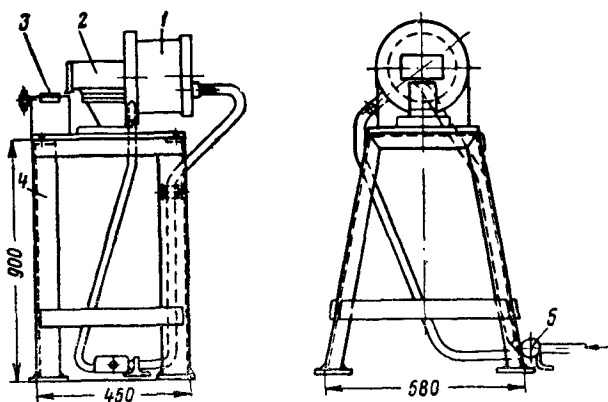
Пневматическое приспособление для обрезки концов проводников якорных катушек тяговых двигателей:
